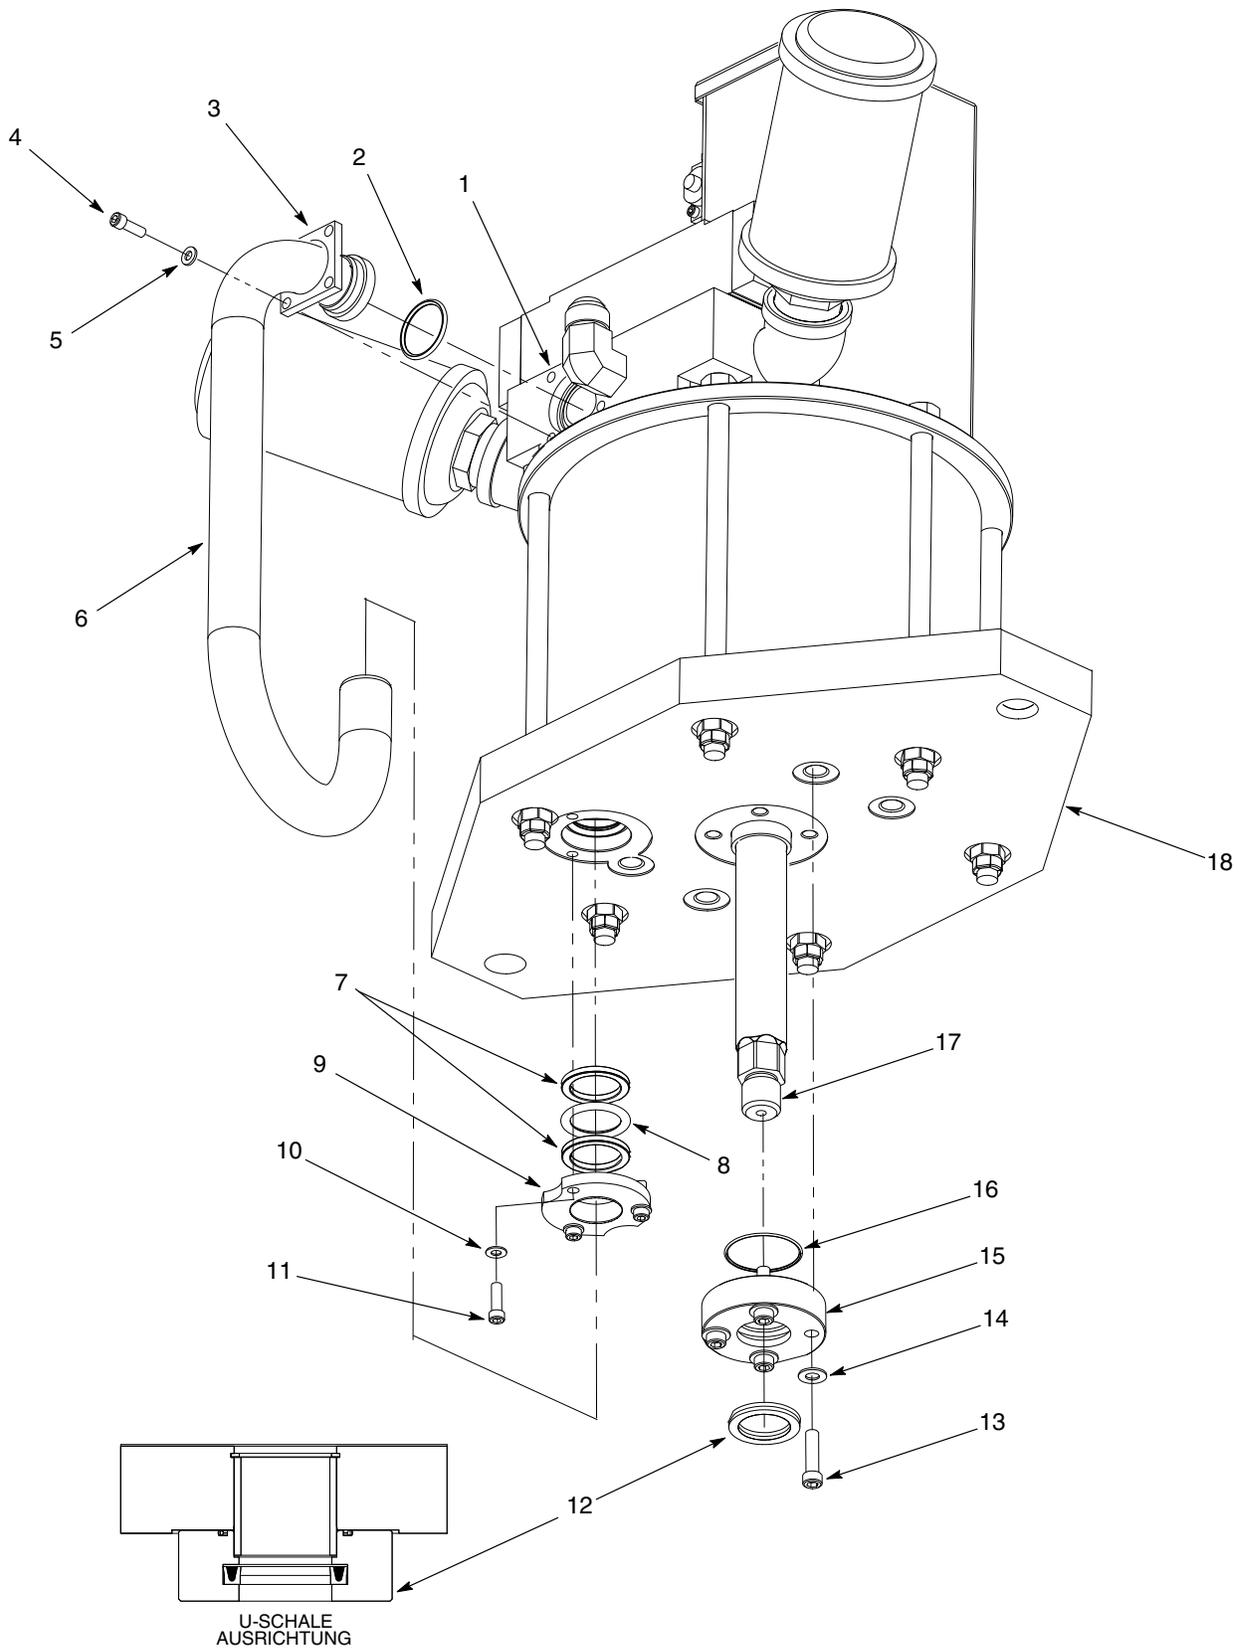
Dichtungen und Ringe der Grundplatte ersetzen
